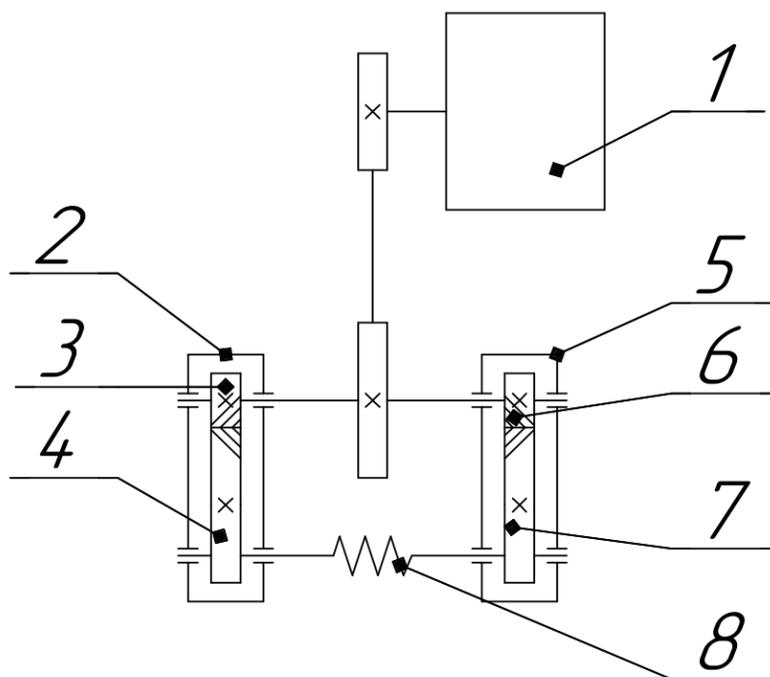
Схема стенда для обкатки зубчатых редукторов:
